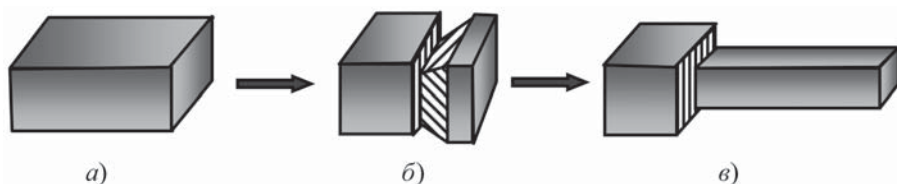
Технологическая последовательность изготовления объемной Т-образной заготовки: а – исходная заготовка; б – заготовка после пережима с четырех сторон; в – заготовка после протяжки
